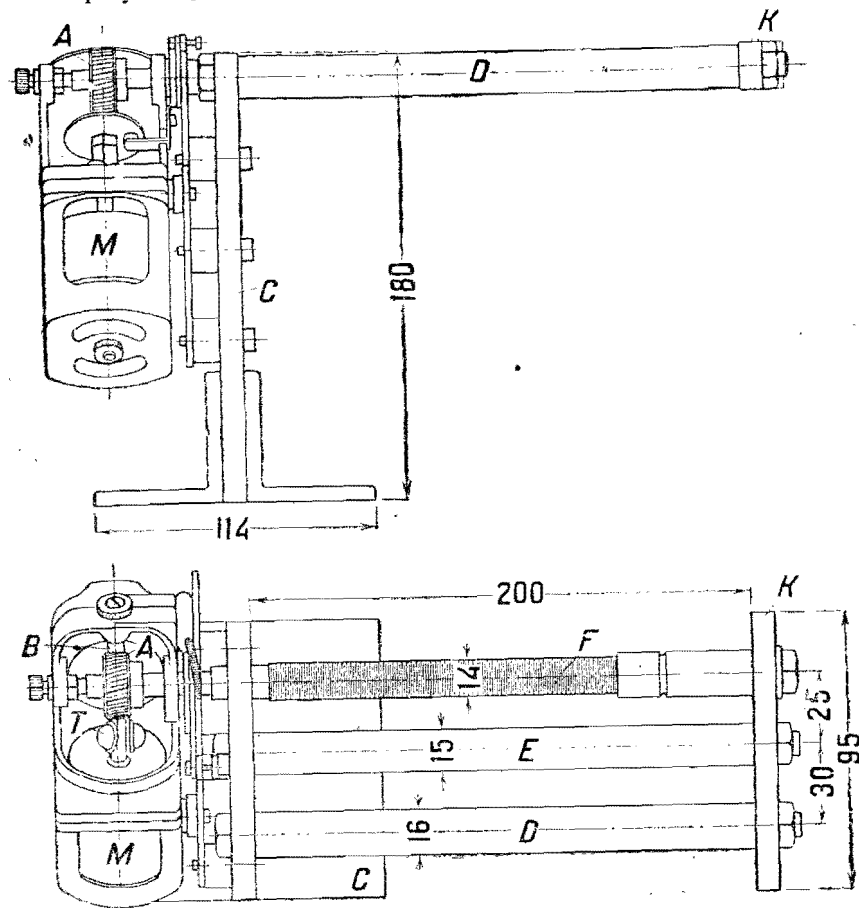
Чертеж приставки для звукозаписи на пластинку.
